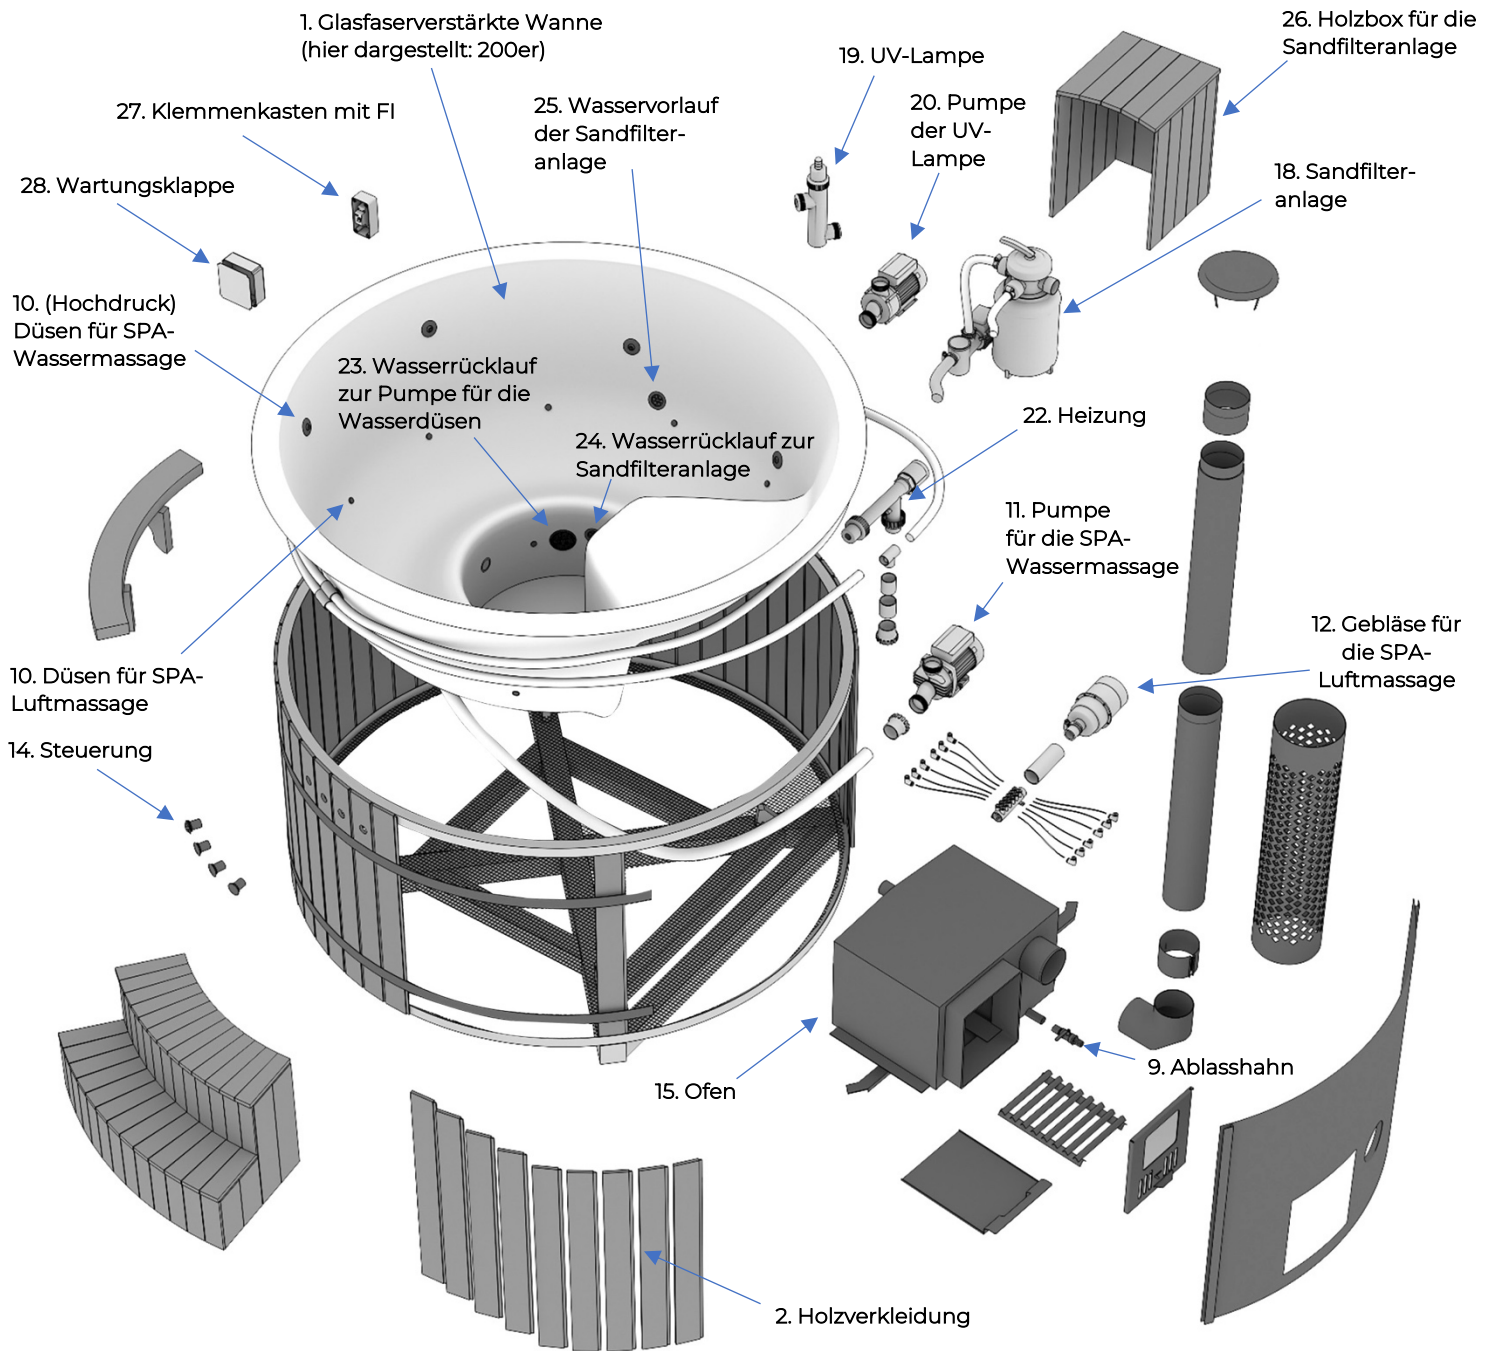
Explosionszeichnung Hot Tub, Ausführungsvariante „SAPHIR“
